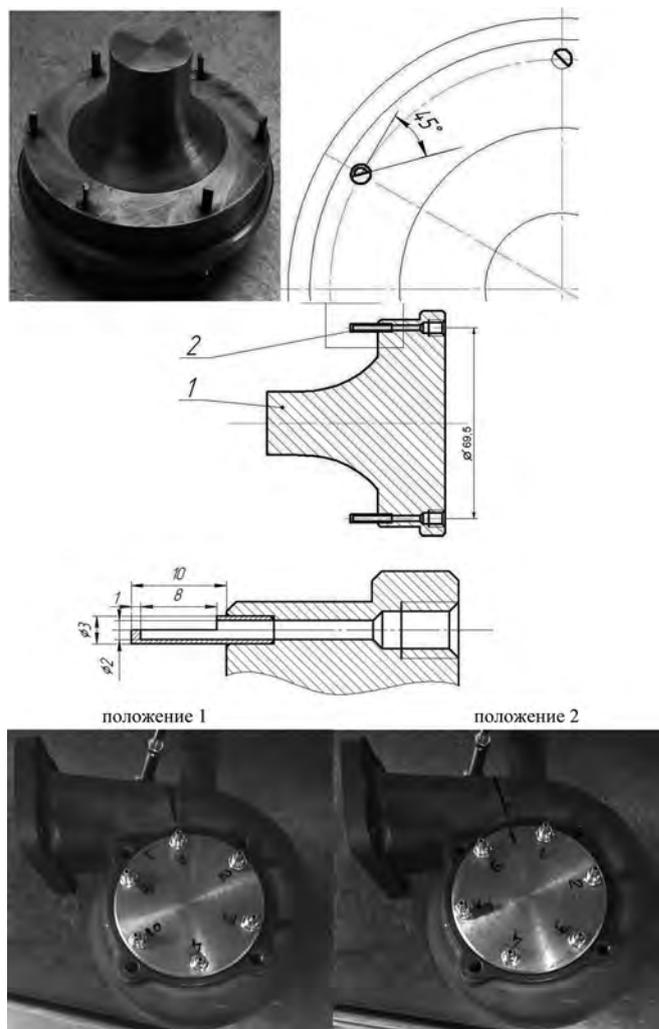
Приспособление для измерения давления. 1 – имитатор рабочего колеса, 2 – отборник
